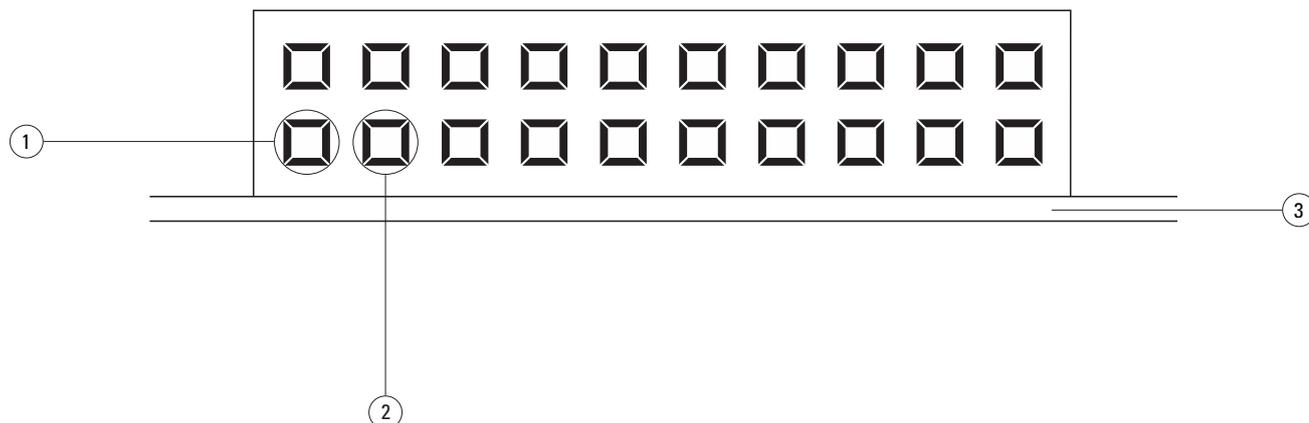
Position von Header J7 im Steuergerät – Ansicht von oben
